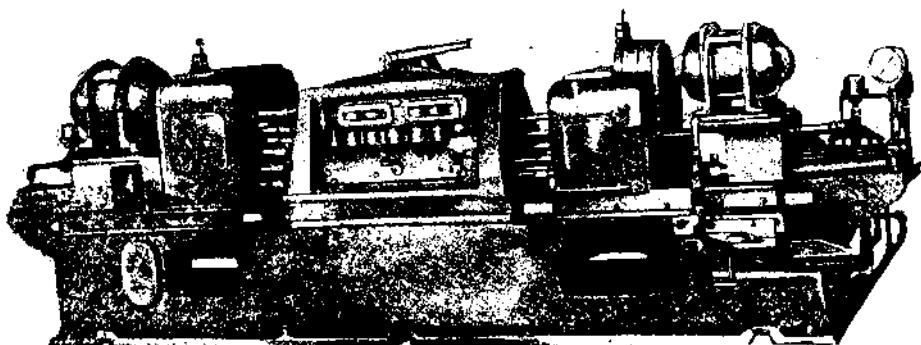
50-шпиндельный сверлильный станок фирмы Barnes.
